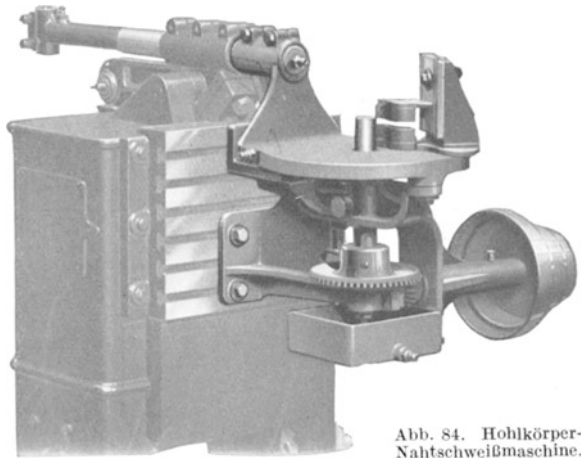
Hohlkörper-Nahtschweißmaschine.
